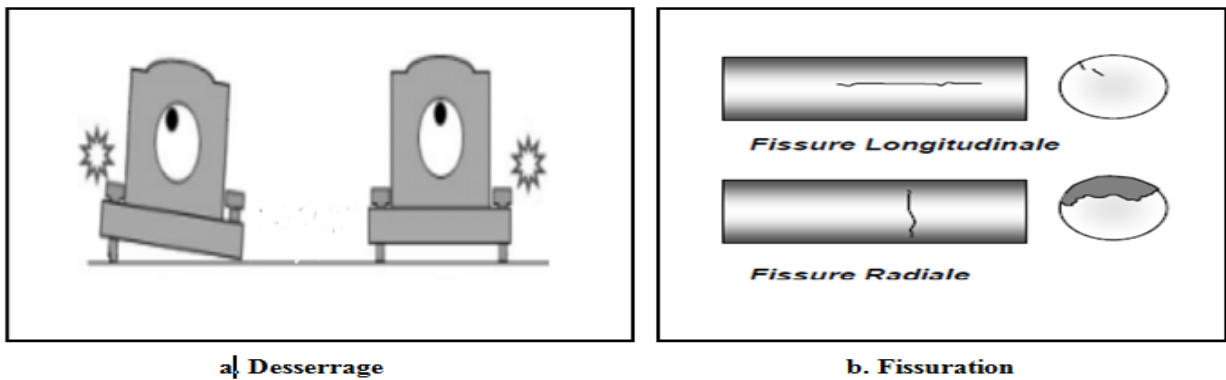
Défauts de desserrage et fissuration.
